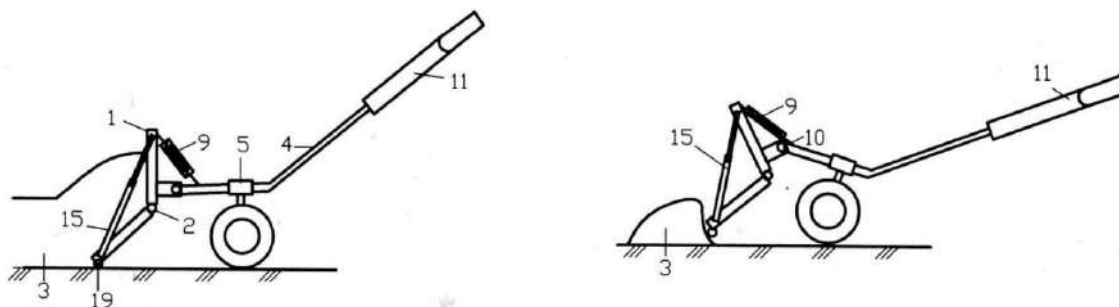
Рычажное снегоуборочное устройство: 1–щит-трансформер; 2 – ось; 3– снег ; 4 – черенок; 5 – патрубок; 6 – ось ОПМ; 7 – колеса; 8 – телескопический кронштейн; 9 – возвратная пружина; 10 – шарнирное соединение; 11 – рукоятка; 12 – винт; 13 – отверстие; 14 – упорный винт; 15 – растяжки; 16 – муфта сцепления; 17 – тросик; 18 – защелка; 19 – ролики.
